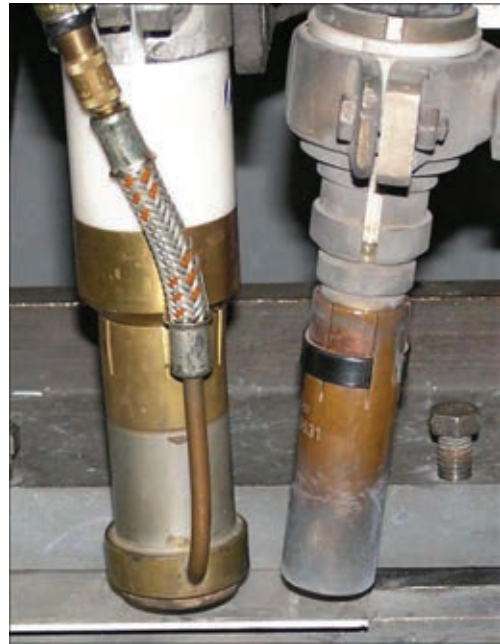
Размещение плазмотрона и горелки плавящегося электрода при комбинированном использовании плазменно-дуговой сварки и дуговой сварки плавящимся электродом
